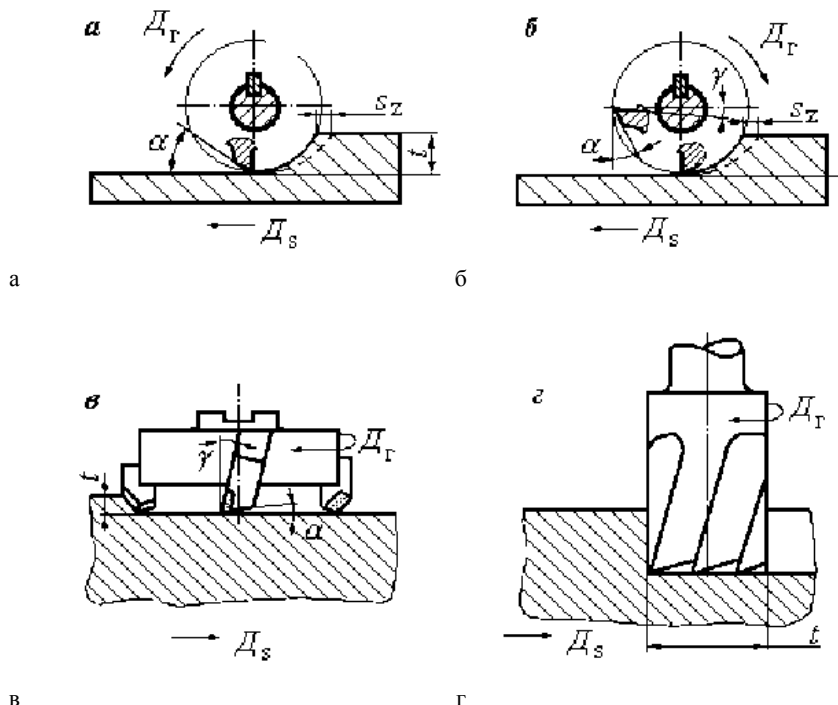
Виды фрезерования: а – против подачи; б – по подаче; в – торцевой фрезой; г – концевой фрезой
